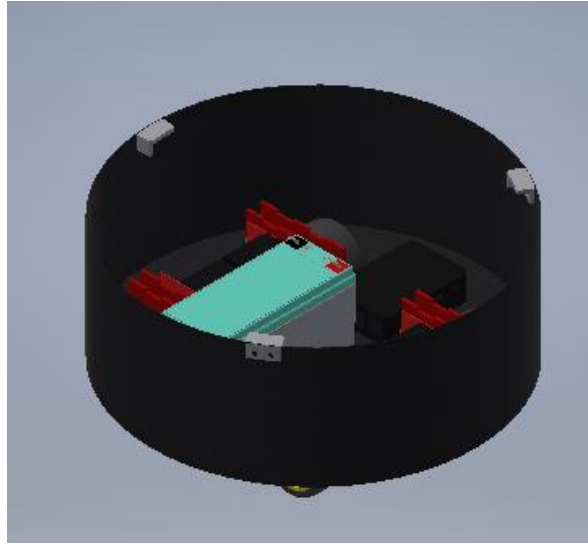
Diseño Final del Módulo de Estructura y Movimiento Vista Isométrica
